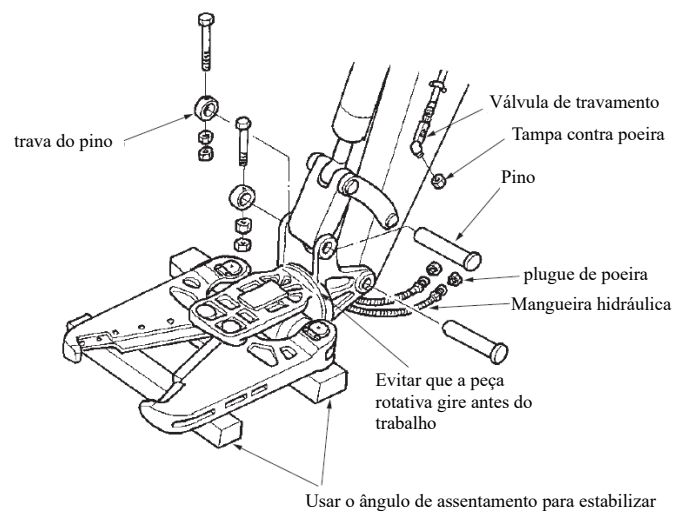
Exemplo de remoção da ferramenta de corte de estrutura de aço
